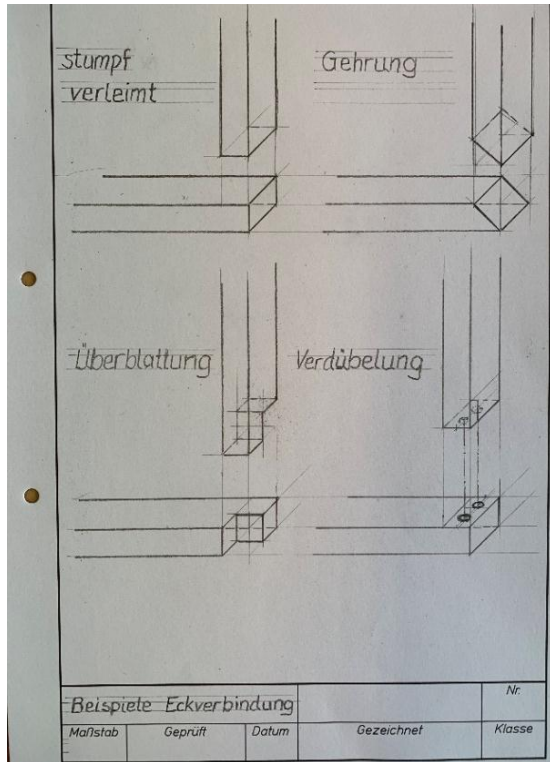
Holzverbindungsmöglichkeiten; Explosionszeichnung
